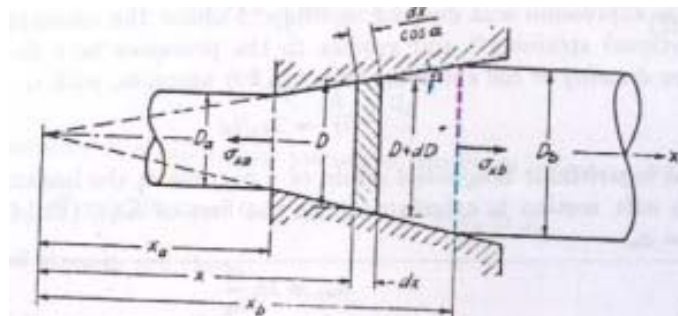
Dimensiones y esfuerzos en la extrusión
